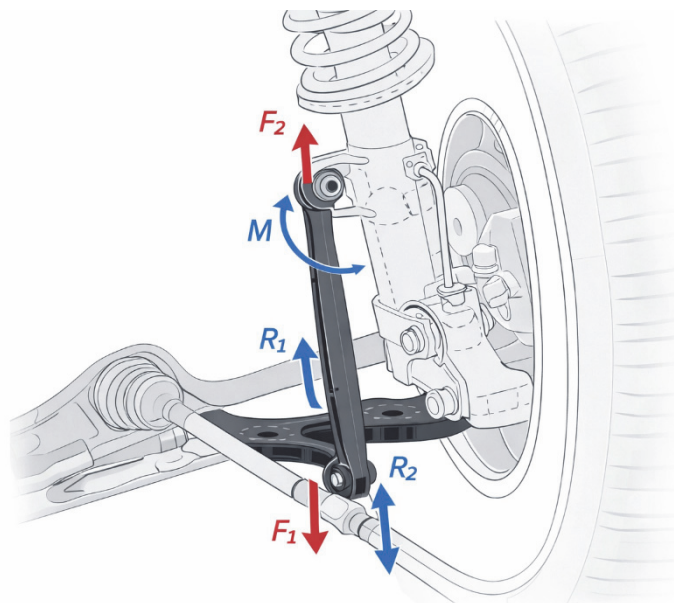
Розрахункова схема силового навантаження важеля стійки стабілізатора
